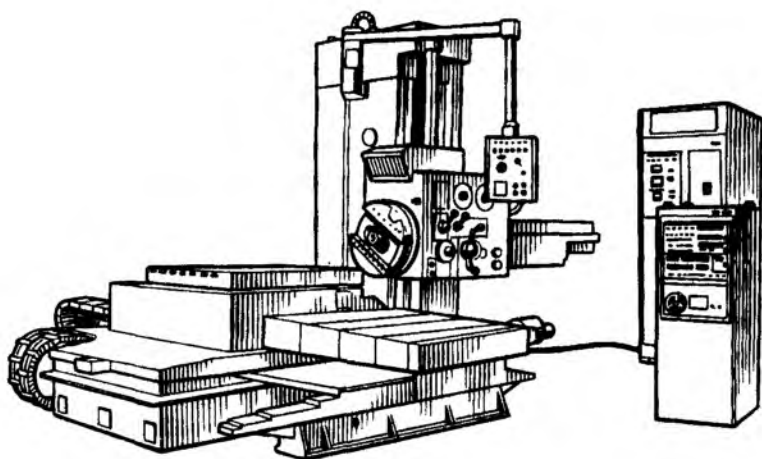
Общий вид горизонтально-расточного станка мод. 2A622Φ2-1
